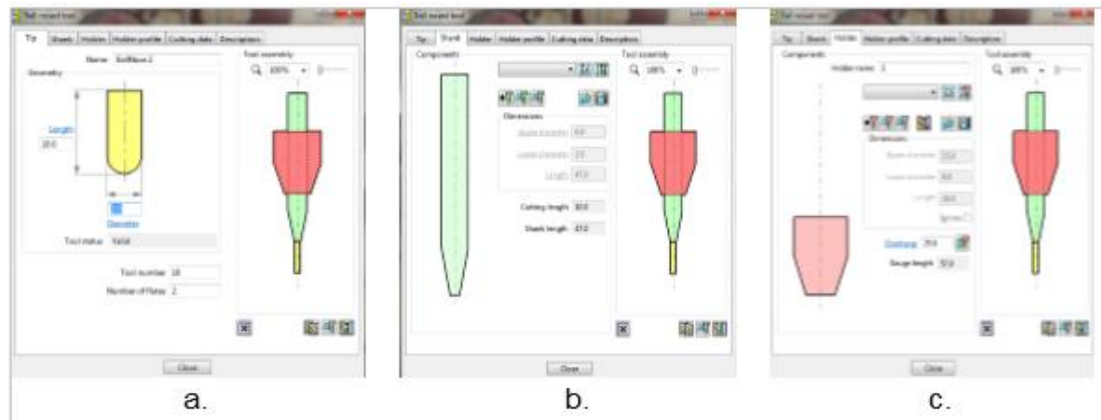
21. (a.) Form Tip Endmill Cutter Diameter 4, (b.) Form Shank Endmill Cutter Diameter 4, (c.) Form Holder Endmill Cutter Diameter 4
